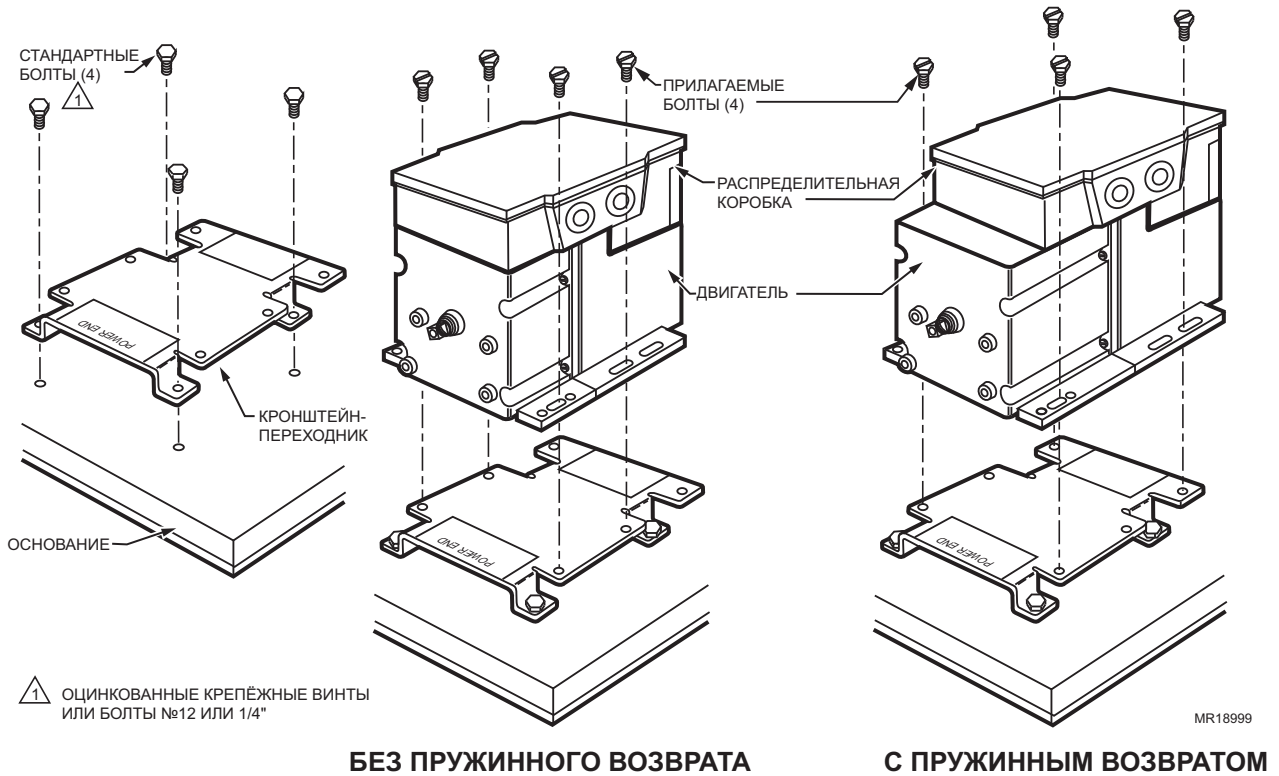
Монтаж двигателя с использованием кронштейна-переходника.
